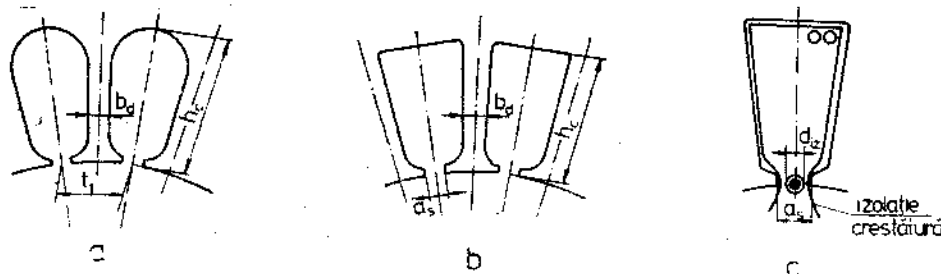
Crestături ovale sau trapezoidale pentru înfășurările din sîrmă rotundă :
